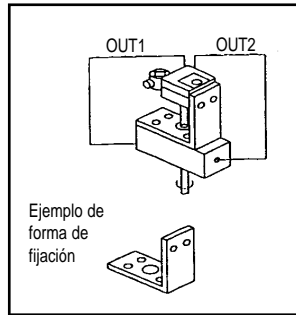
Ejemplo de montaje mediante el tornillo lateral del posicionador
